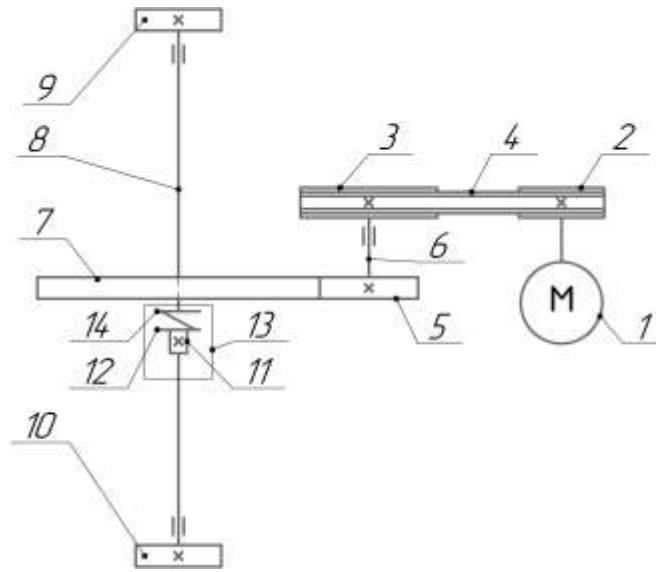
Кінематична схема привода круглов'язальної машини: 1- електродвигун; 2, 3- ведучий та ведений шківни клинопасової передачі; 4- паси; 5- ведуча шестерня; 6- проміжний вал; 7- зубчасте колесо; 8- приводний вал; 9, 10- шестерні; 11- пружна запобіжна муфта; 12, 14- пів муфти.
